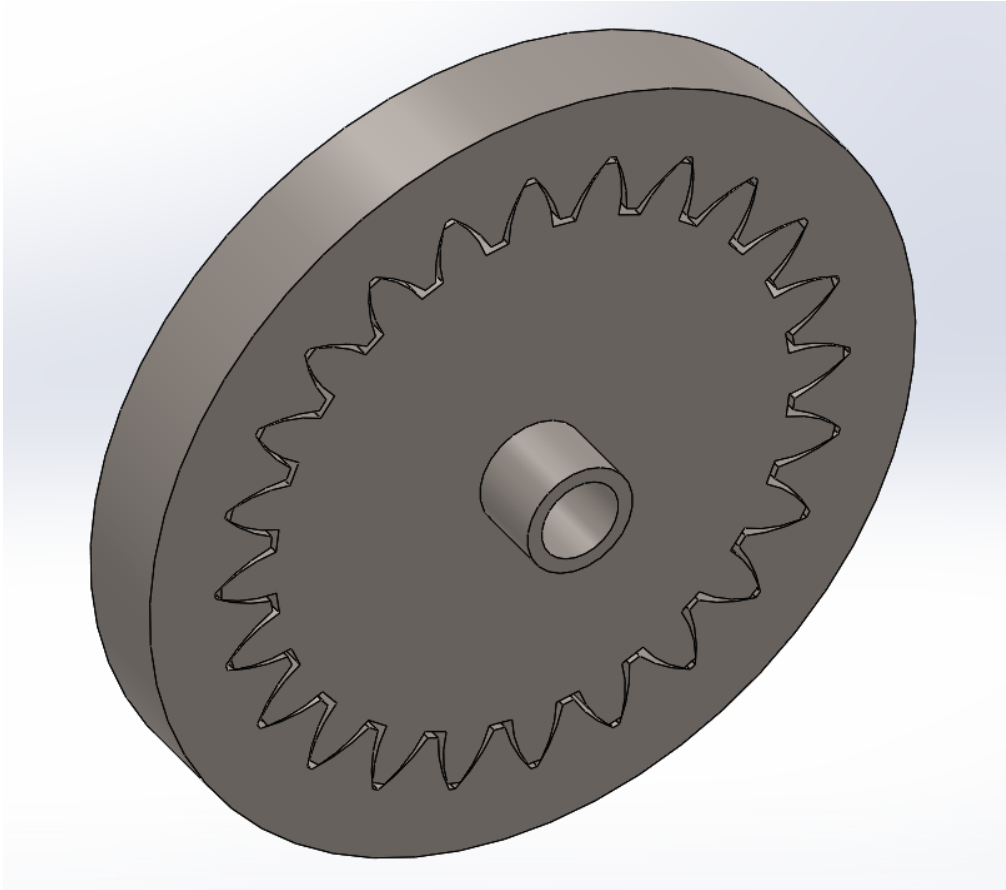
Conjunto de engranajes que mueven el cabezal por dentro.
